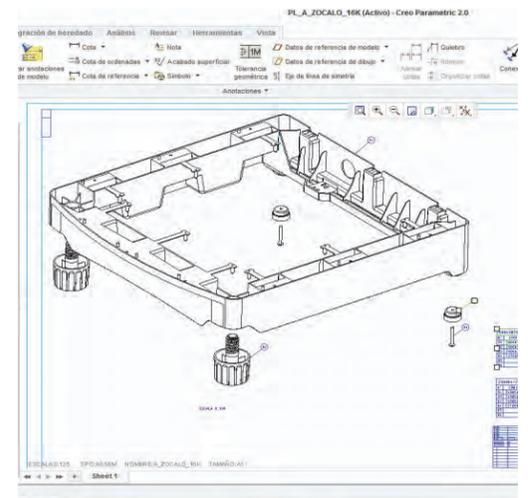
Creo parametric Planimetría Zocalo Fuente: Autoría propia
